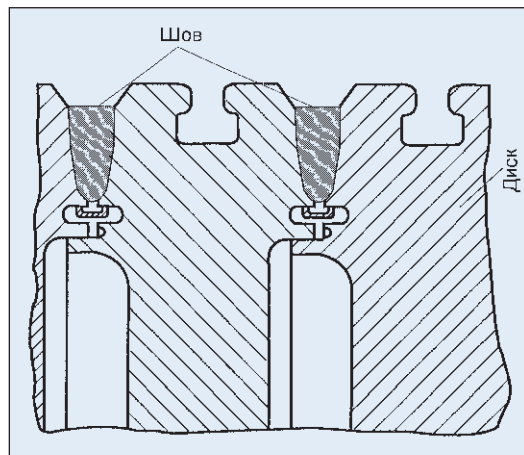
Схема расположения сварных швов относительно пазов для рабочих лопаток
